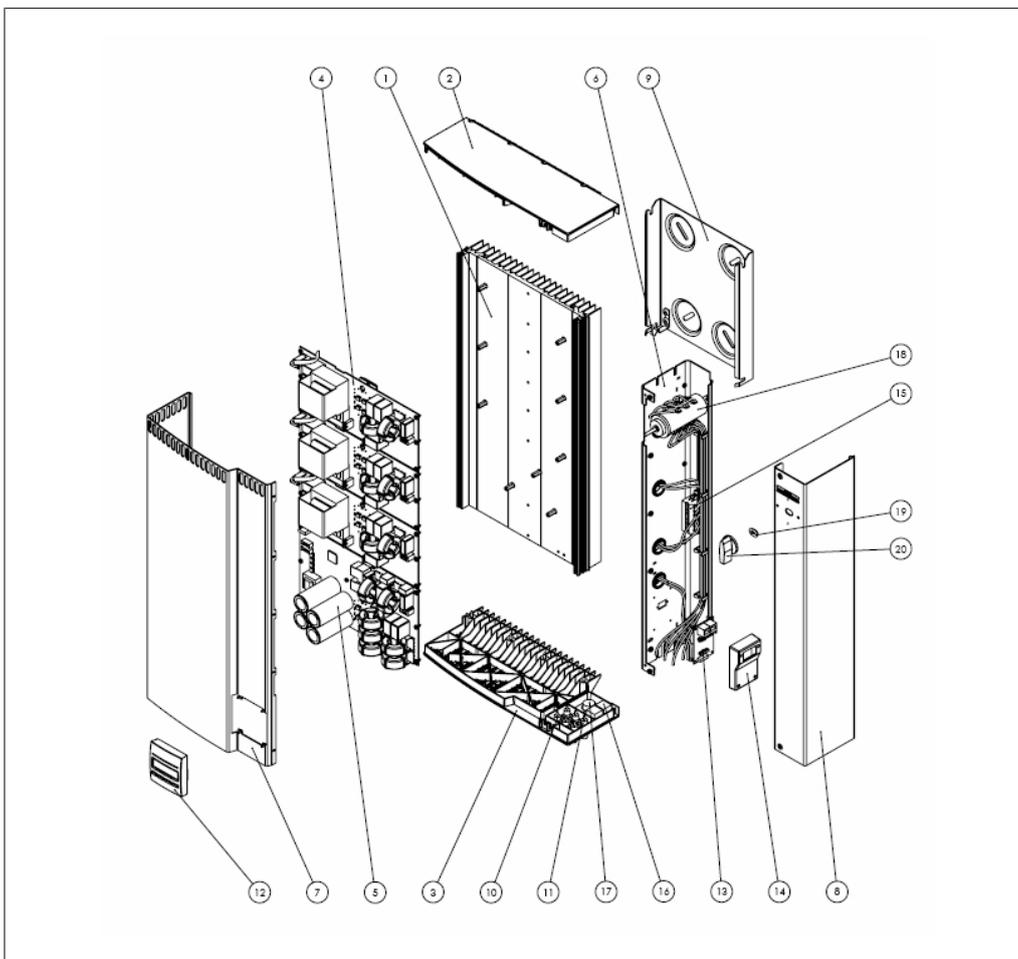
Explosionszeichnung des ULX 5400i
